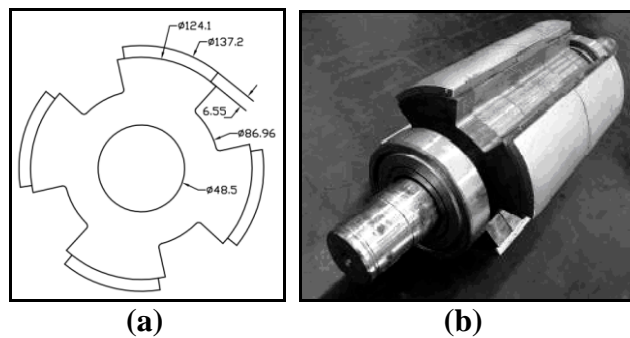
Rotor de polos salientes – (a) Desenho esquemático – (b) rotor montado [11]
